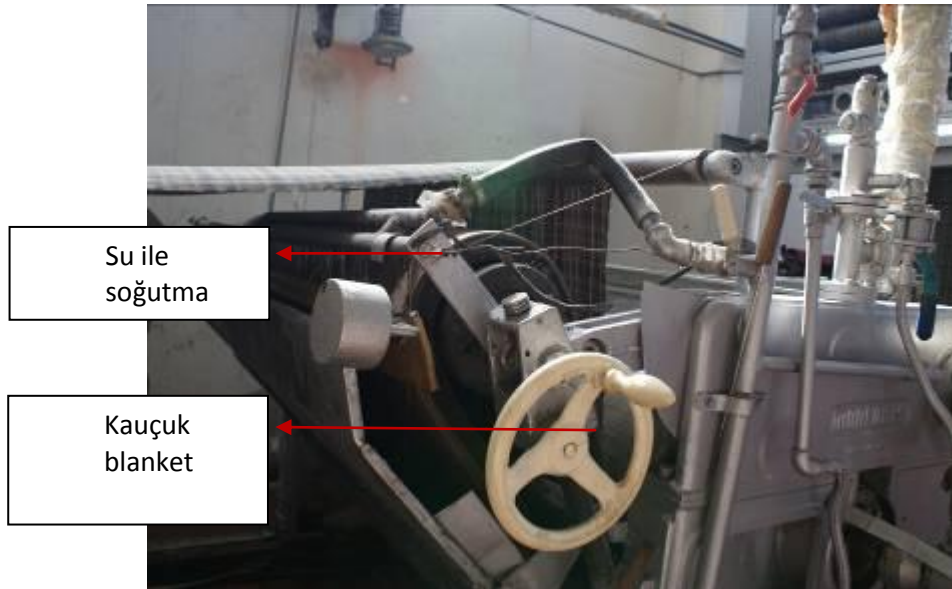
Örne kumaş sanfor makinesinde kauçuk blanket
